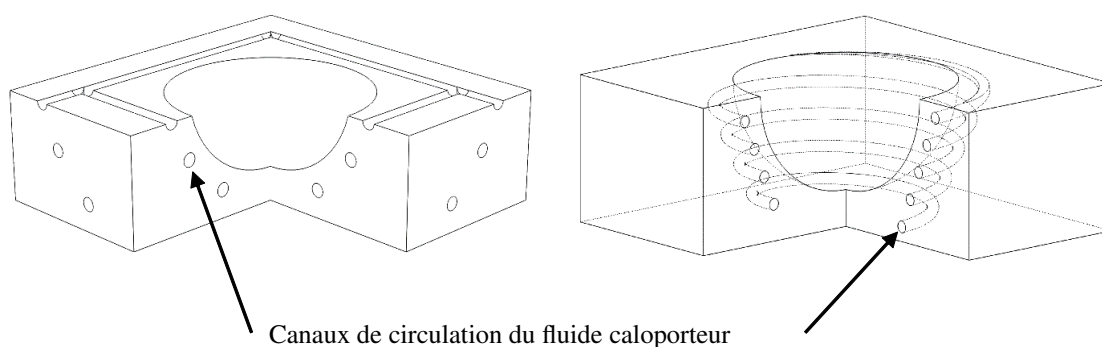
Canaux droits traditionnels (gauche) - Canaux conformables (droite)
